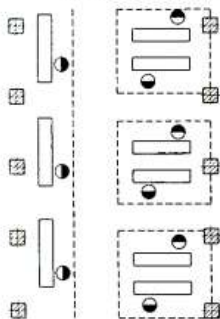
Поздовжнє і поперечне розташування верстатів у прогоні
